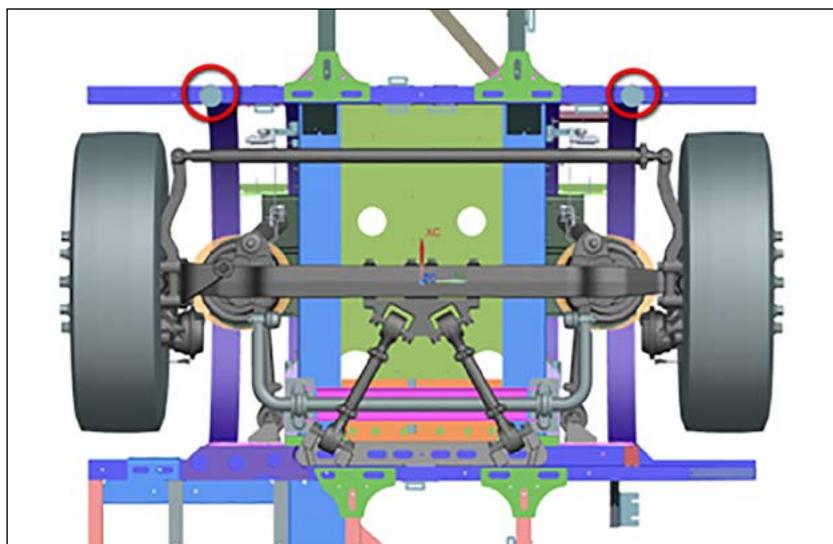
Pontos de apoio para elevação do eixo dianteiro
